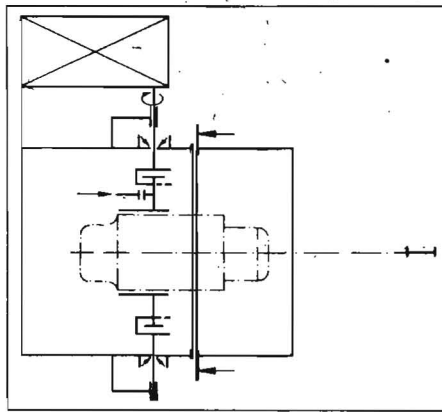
Prinzipskizze einer Anlage für die demontagefreie Innenreinigung von Motoren
